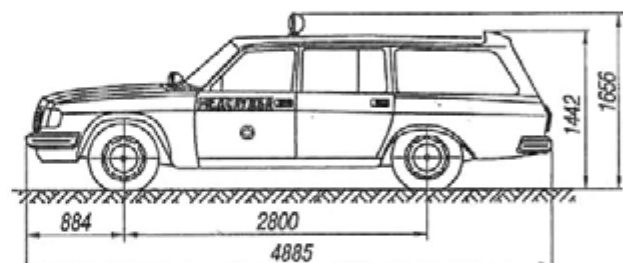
Автомобиль "Волга" ГАЗ-31023 и его габаритные размеры
